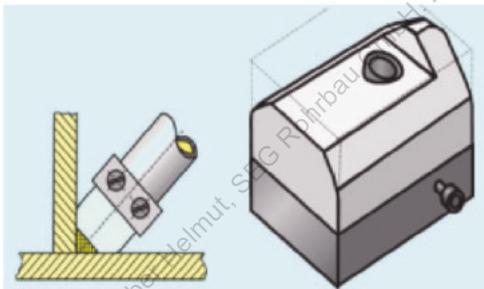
, Schweißschuh für Kehlnaht
